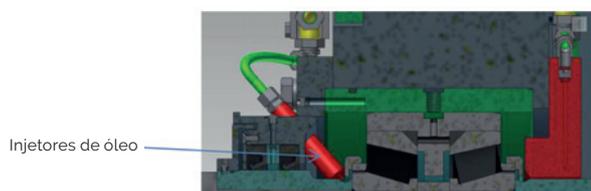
Lubrificação da caixa de engrenagens do bobinador.
